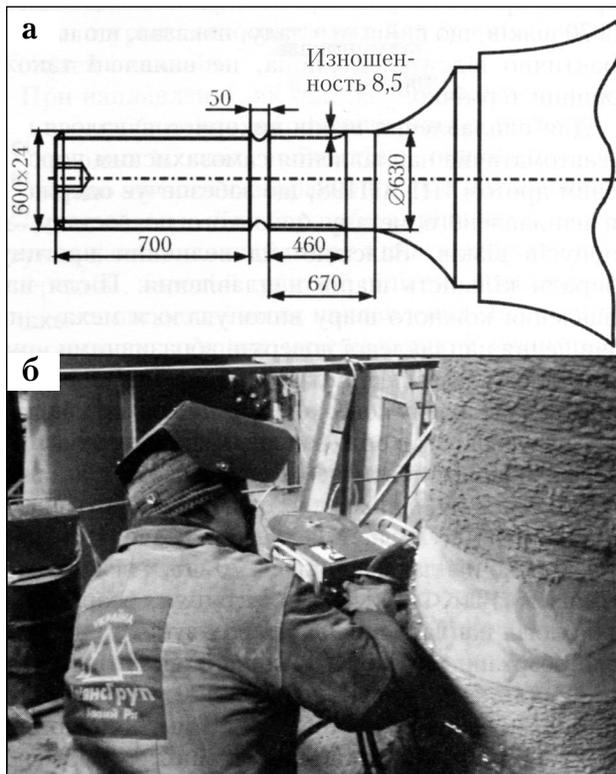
Восстановление вала конусной дробилки дуговой наплавкой: а – изображение восстанавливаемой поверхности конуса; б – полуавтоматическая наплавка изношенной поверхности конуса
